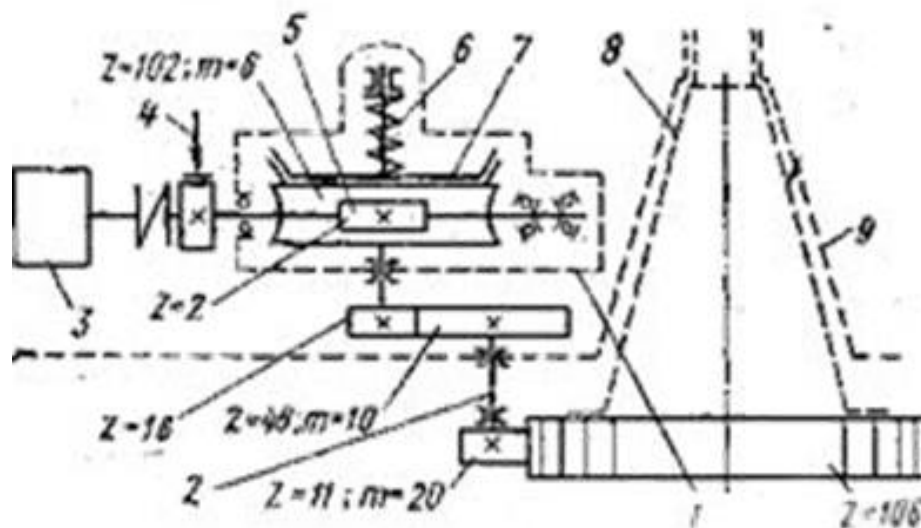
Кінематична схема механізму повороту крана-навантажувача КП-8: 1 - редуктор, 2 - вал, 3 - електродвигун, 4 - гальмо, 5 - черв'ячний вал, 6 - пружина, 7 - натискним диск, 8 - неповоротний оголовок, 9 - поворотна частина оголовка.
